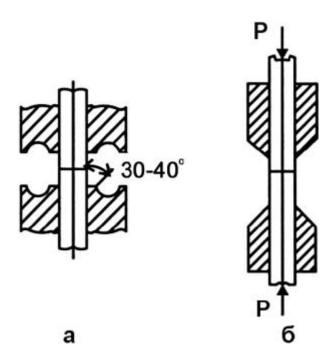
Схема зажимов для стыковой холодной сварки: 1-c затрудненным истечением металла;
